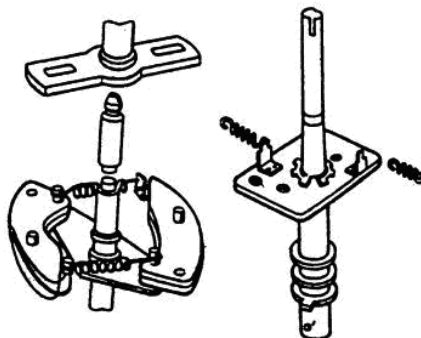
Конструкция центробежного регулятора распределителя зажигания.
